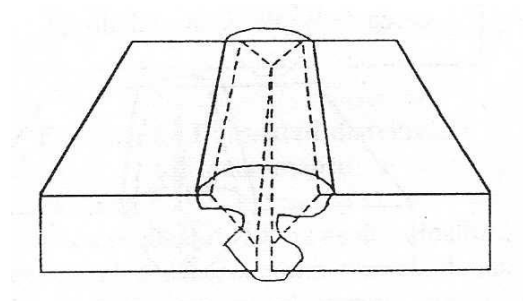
Socavado en el pie del cordón de soldadura. [22]
